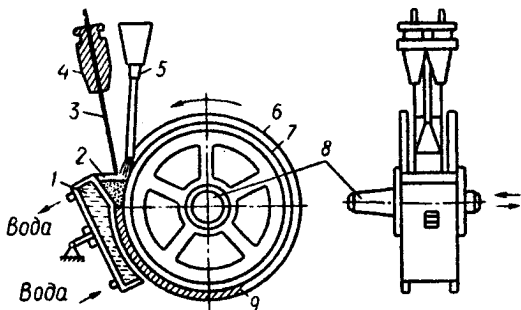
Схема електрошлакового наплавлювання опорних котків:
